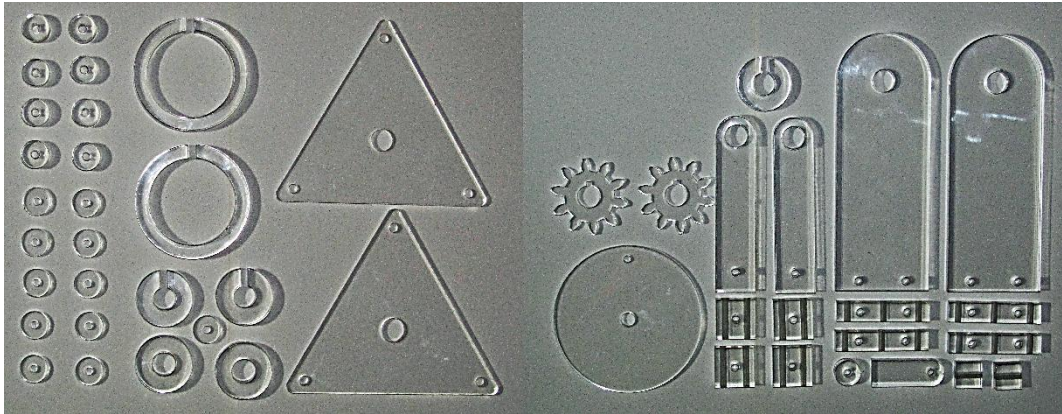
File Corel Draw untuk Cutting Laser Acrylic Sign Board 3 mm
